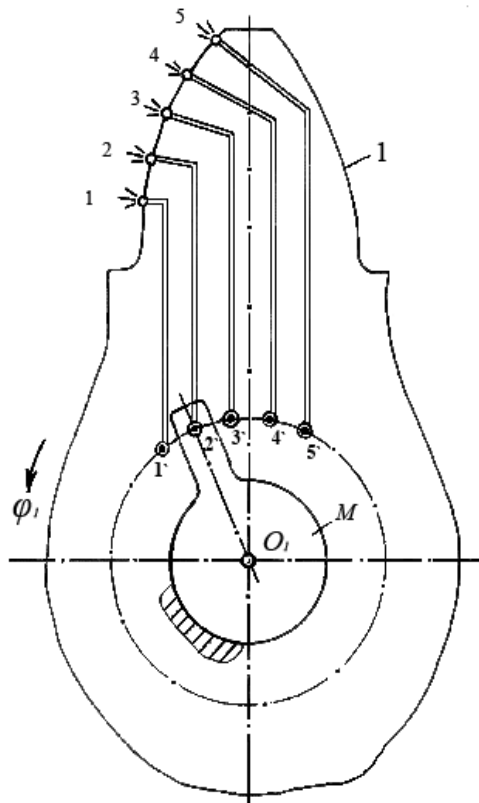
Зубчатое колесо передачи с гидростатической смазкой и постоянной скоростью контактной точки по профилю зуба
